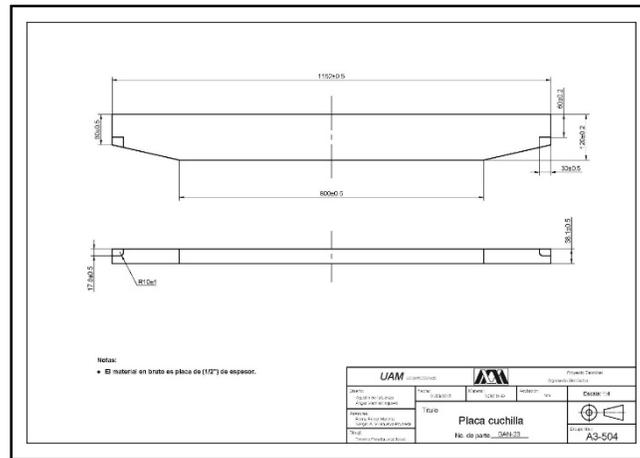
Plano A3-504 Placa cizalla generado en AutoCAD.
